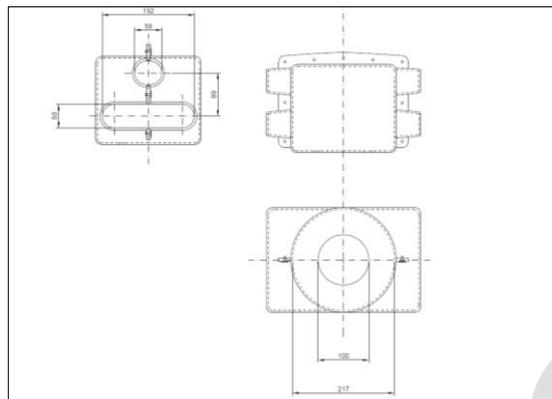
Plano de forro aislante para conjunto de suspensión de catenaria de 3kV
